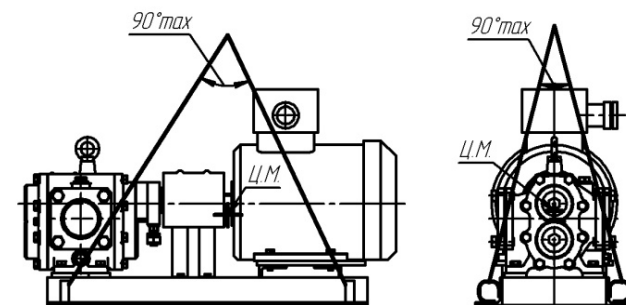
Габаритный чертеж насоса с электродвигателем, рамой и защитным кожухом
